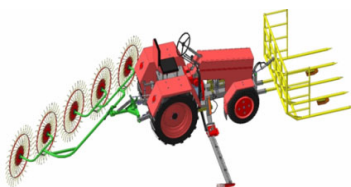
3D модель комбинированного агрегата для заготовки кормов
